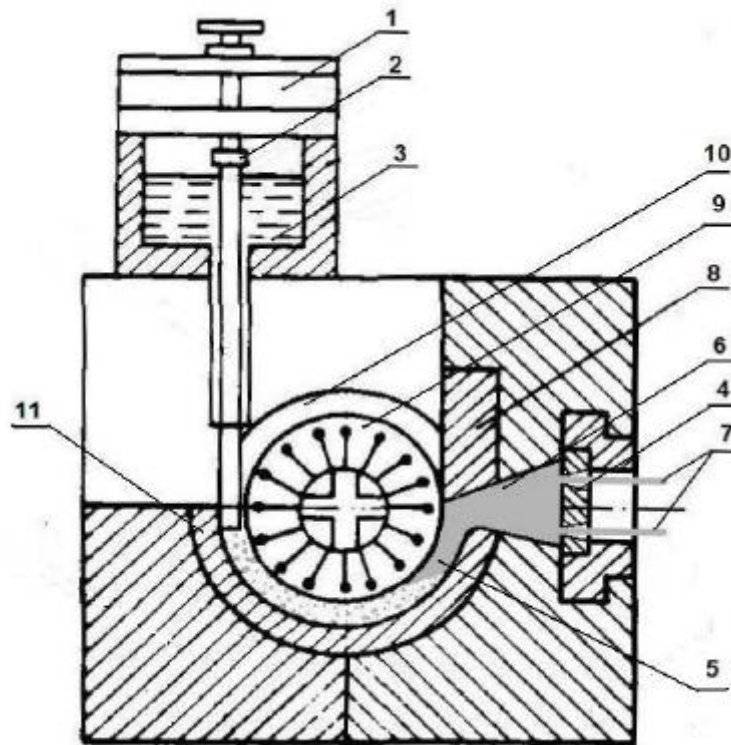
Схема процесса непрерывного прессования Конформ-Кастэкс полых профилей из жидкого металла: 1 – дозатор; 2 – устройство регулирования расхода жидкого металла; 3 – жидкий металл; 4 – матрица; 5 – фронт кристаллизации; 6 – камера сварки; 7 – полые профили; 8 – упор; 9 – колесо; 10 – кольцевая канавка; 11 – кольцевая вставка
